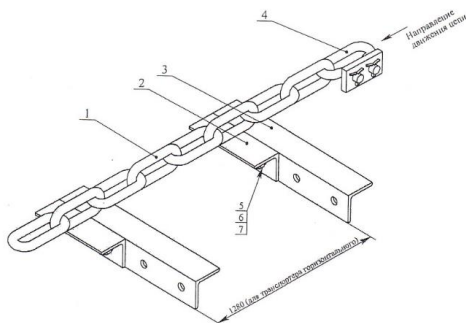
Рабочий орган транспортера ТСН-160: 1 – цепь круглозвенная; 2 – кронштейн; 3 – скребок; 4 – звено соединительное; 5 – болт М12х30; 6 – гайка М12; 7 – шайба пружинная 12.65Г.016
